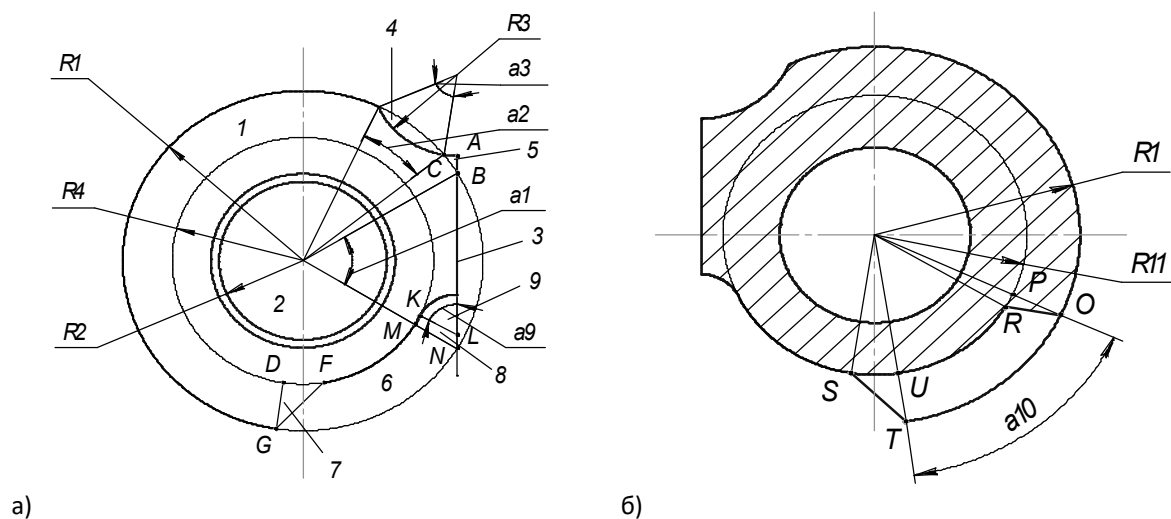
Схема вимірювання розмірів втулки: а). основний вигляд; б) – вигляд А
